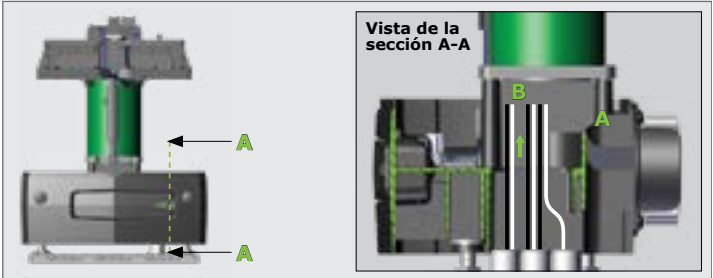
ENRUTAMIENTO DE CABLES PARA RETROAJUSTE CON CABLES MÁS CORTOS
